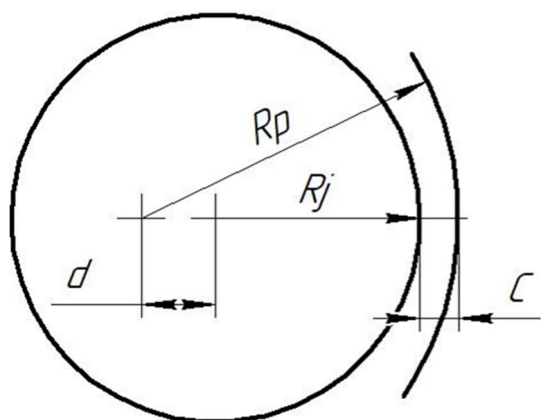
Принципова схема пелюсткового підшипника
